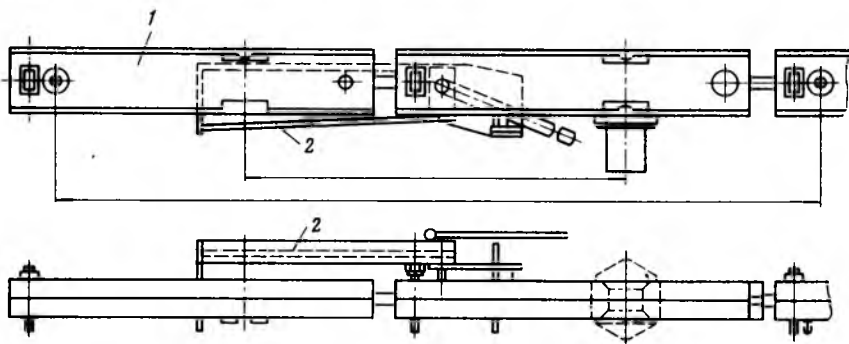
Металлический шарнирный верхняк ВВ-30М:
